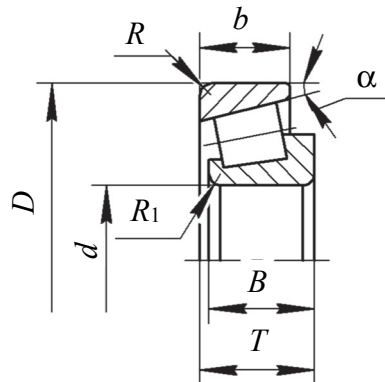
Габаритные размеры роликовых конических однорядных подшипников (по ГОСТ 333–79)
